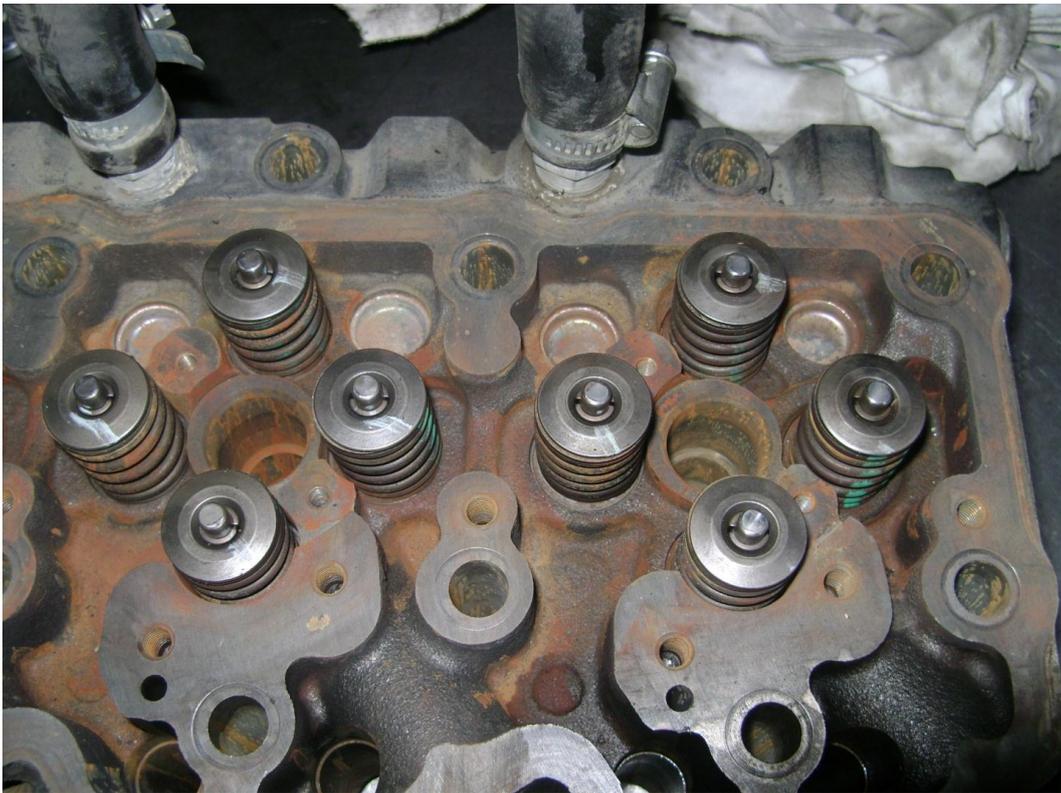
Расположение клапанов головки блока двигателя *Cummins
